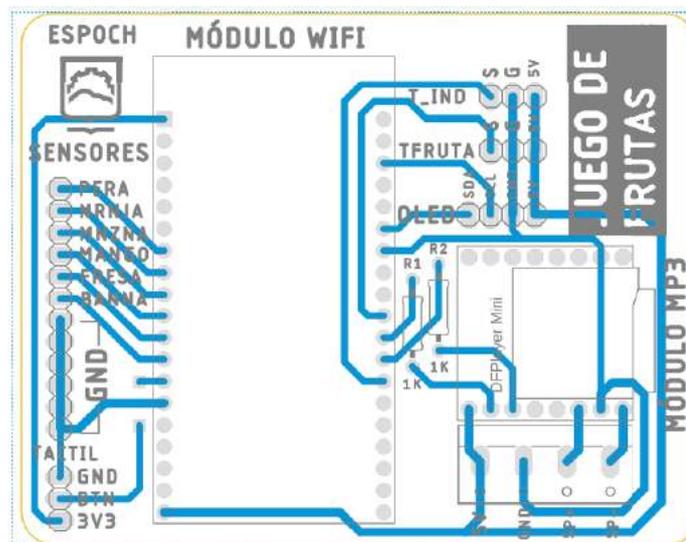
Diseño de la placa PCB del módulo de frutas
